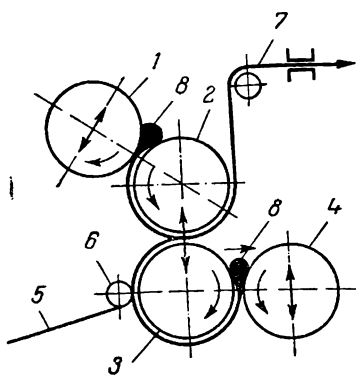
Схема двухсторонней обкладки корда резиновой смесью на четырехвалковом Z-образном каландре:
